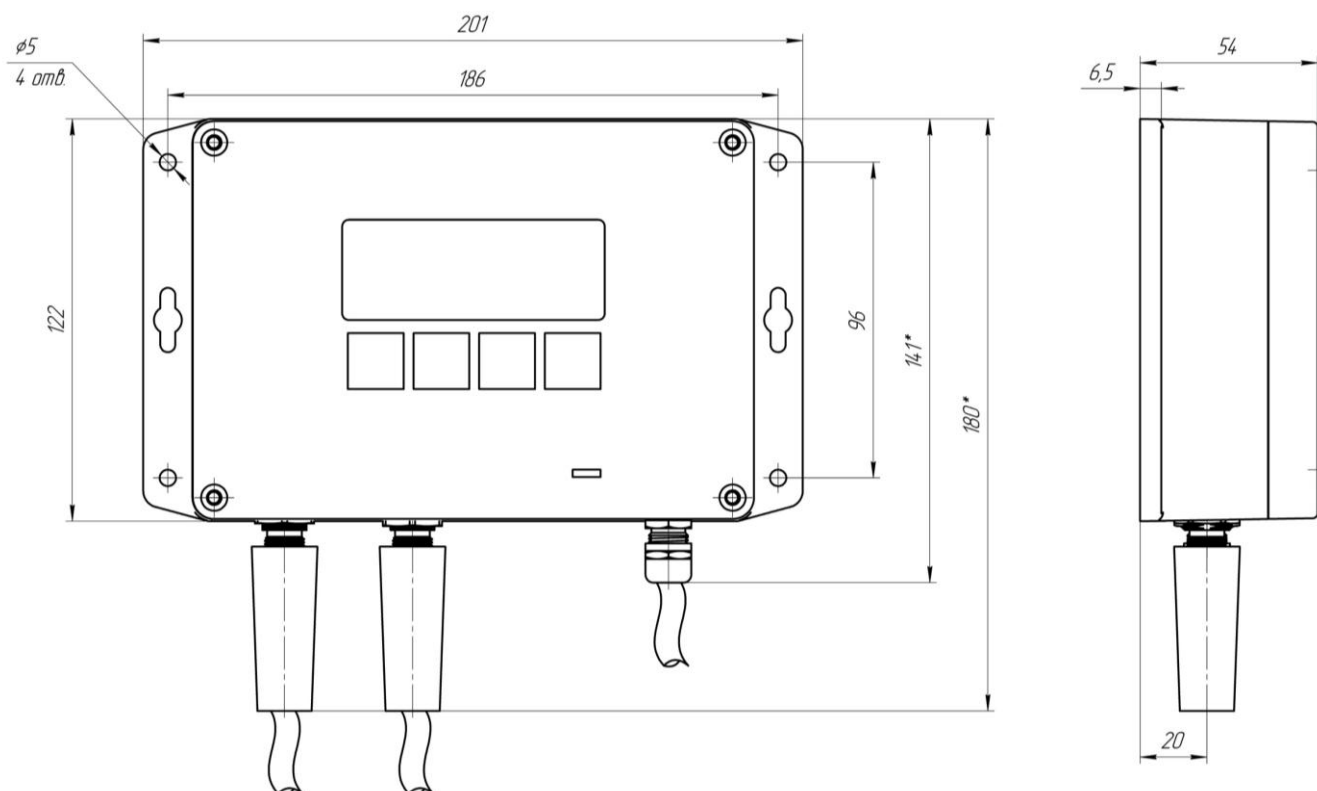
Габаритный чертёж ВЭП СКЭ версии 2
